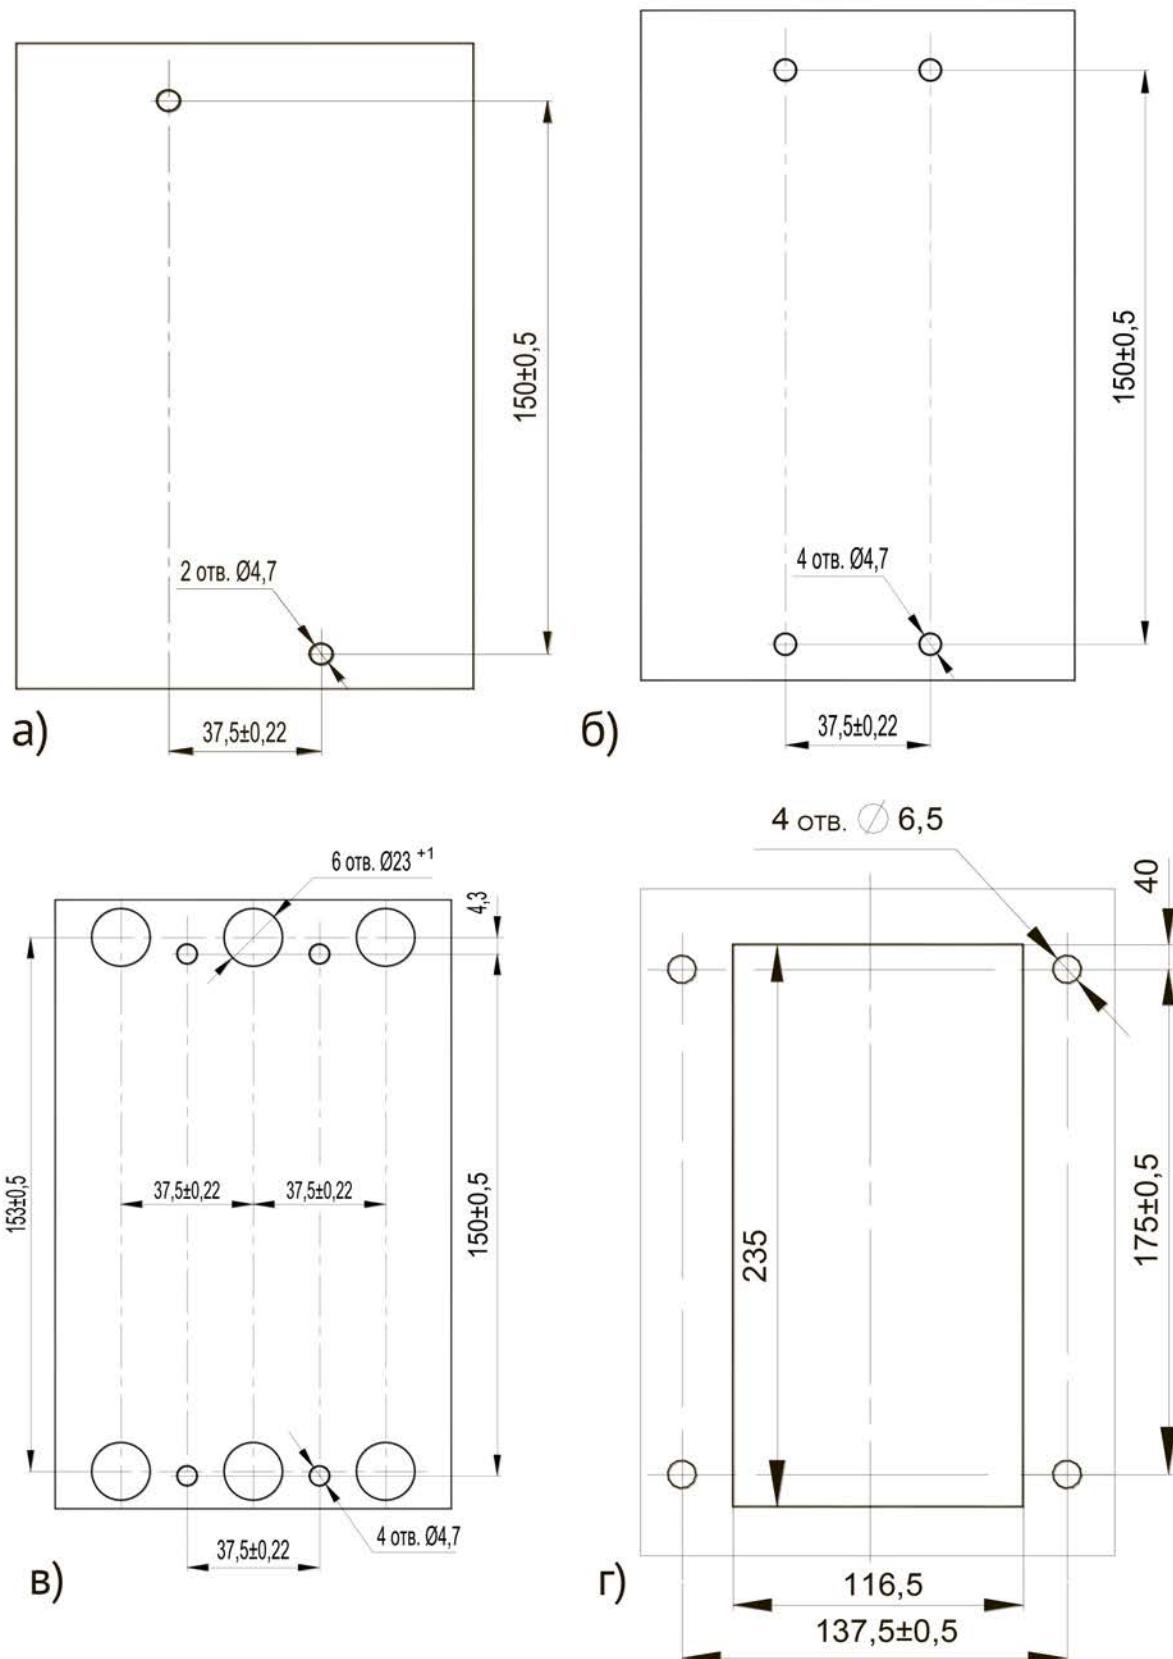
Расположение отверстий для крепления выключателя
